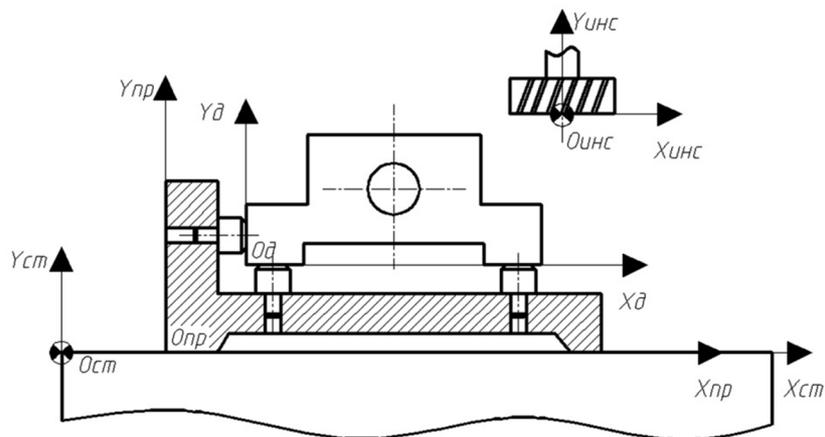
Проектная схема обработки заготовки на операции фрезерования
